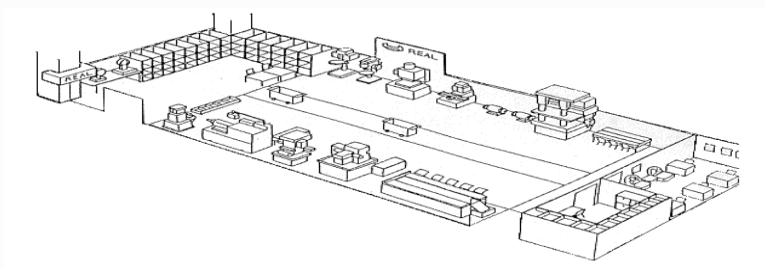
Distribución de planta por producto. Fuente: Imágenes de Google (2013).
